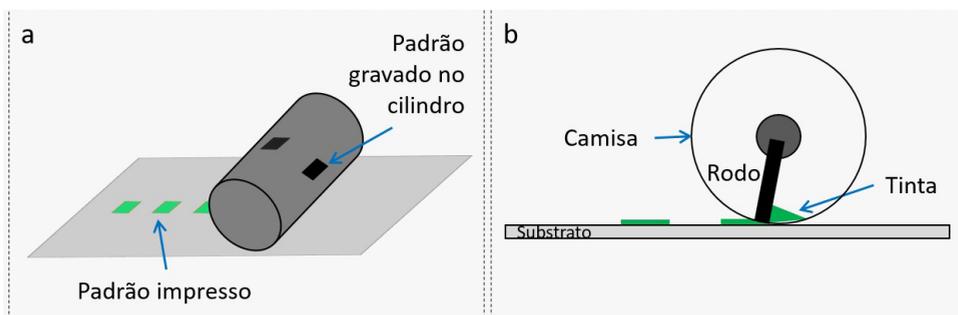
Serigrafia rotativa. a) Representação do processo de impressão; e b) Corte transversal do cilindro de impressão em que aparece a posição do rodo de raspagem de tinta e camisa de impressão do padrão.
